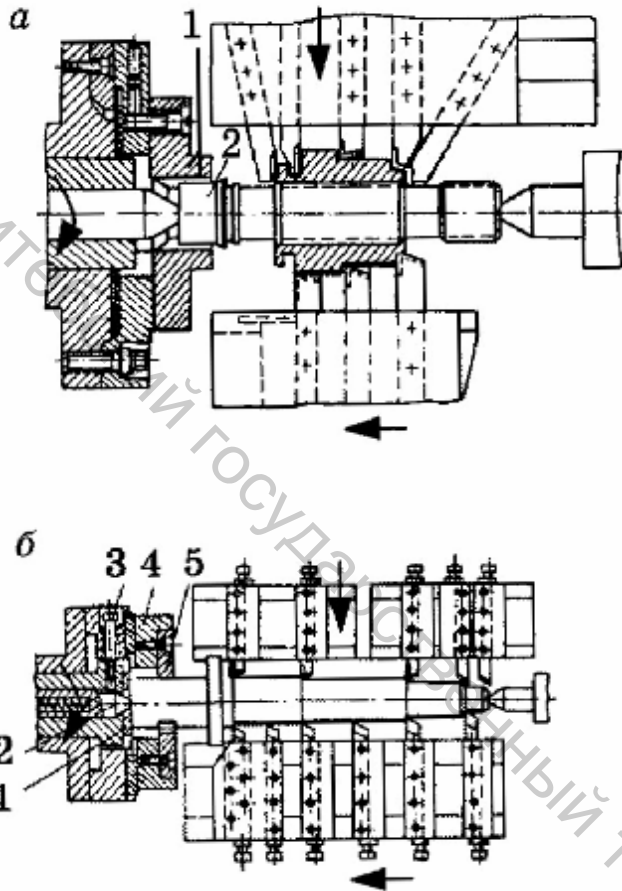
Схема наладки многорезцового станка для обтачивания: а- двухвенцового зубчатого колеса, б- ступенчатого вала
